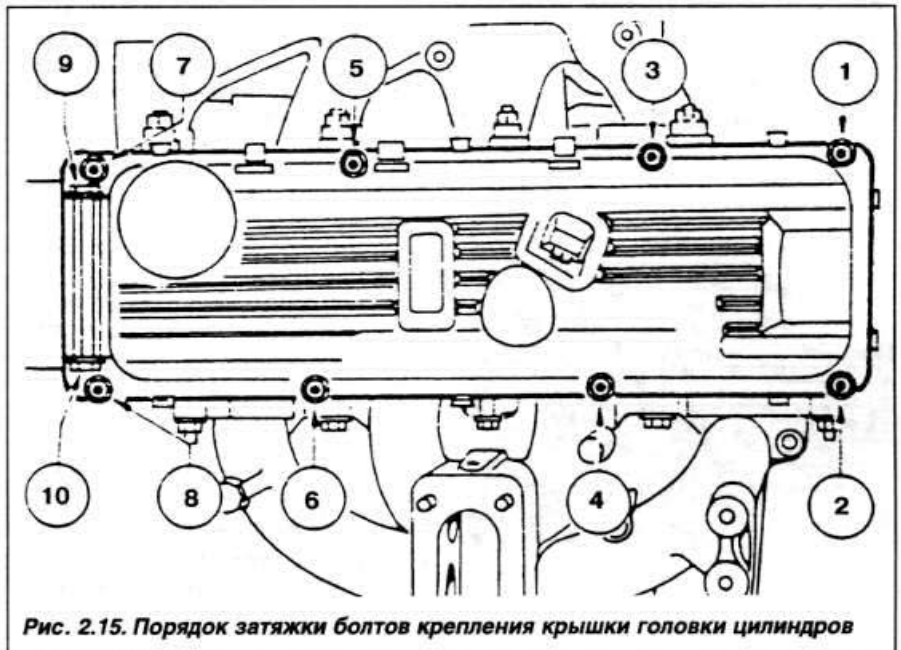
Порядок затяжки болтов крепления крышки головки цилиндров
